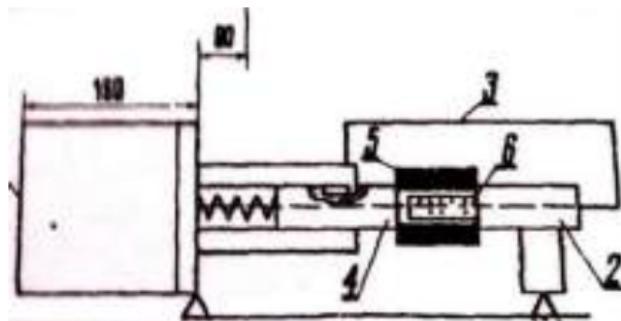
Кінематична схема устаткування гідротермічної роздачі (ГТР) поршневих пальців: 1 – пневмоциліндр; 2 – нерухомий центр; 3 – тяга гідроклапана; 4 – рухливий центр; 5 – поршневий палець; 6 – спрейєр
